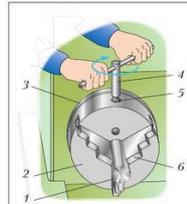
Установка заготовок в трёхкулачковый патрон: 1 – заготовка; 2 – корпус патрона; 3 – планшайба; 4 – ключ; 5 – отверстие под ключ; 6 – кулачки
